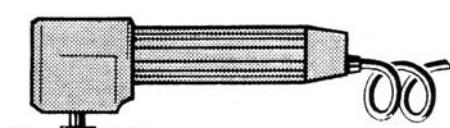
Outil pneumatique rotatif avec renvoi d'angle : surfaceuses, polisseuses à disque...
